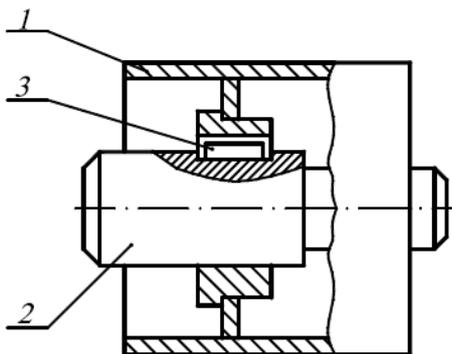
Изображение сварной сборочной единицы на сборочном чертеже.
